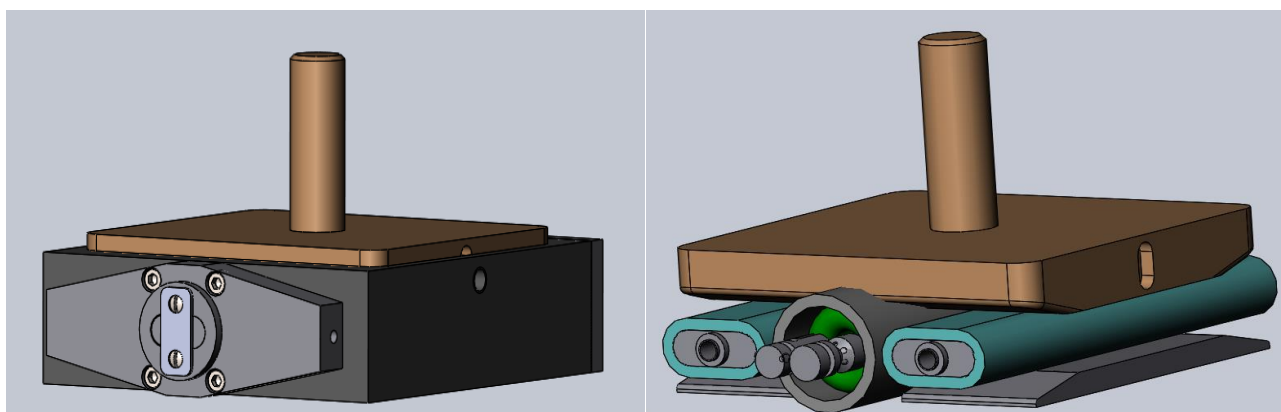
Сборка амортизатора с обратным клапаном
